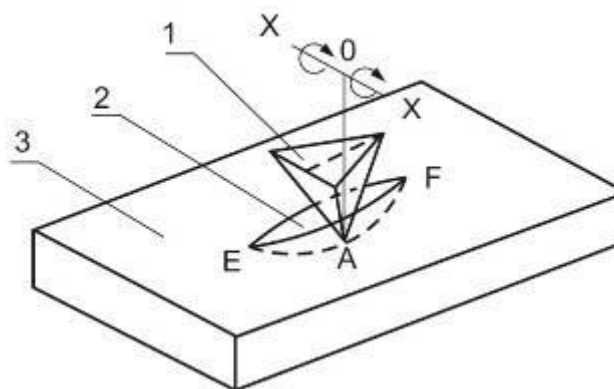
Схема вырезания лунки: 1 - трехгранный алмазный резец; 2 - лунка; 3 - поверхность трения детали (образца); X - ось вращения резца; E - длина лунки; OA - ось вращения вершины резца.
